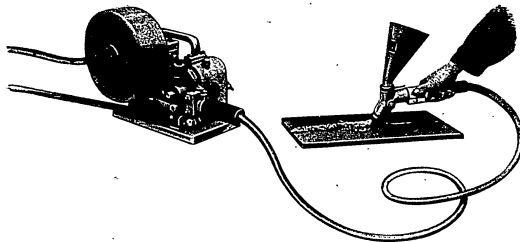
Подводящий механизм полуавтомата ПШ-5 и держатель ДШ-5 при сварке стыкового шва
